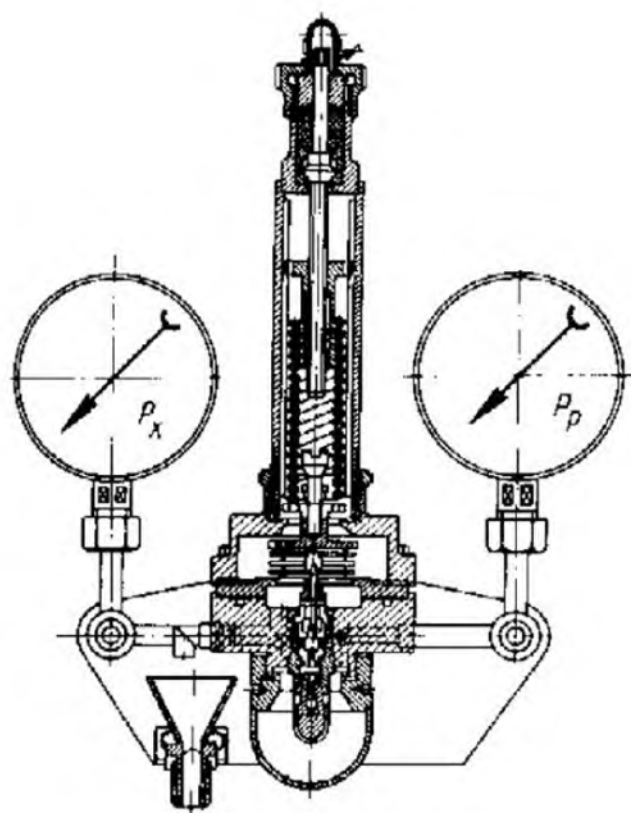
Регулирующий прибор РД-3а односильфонной сборки
